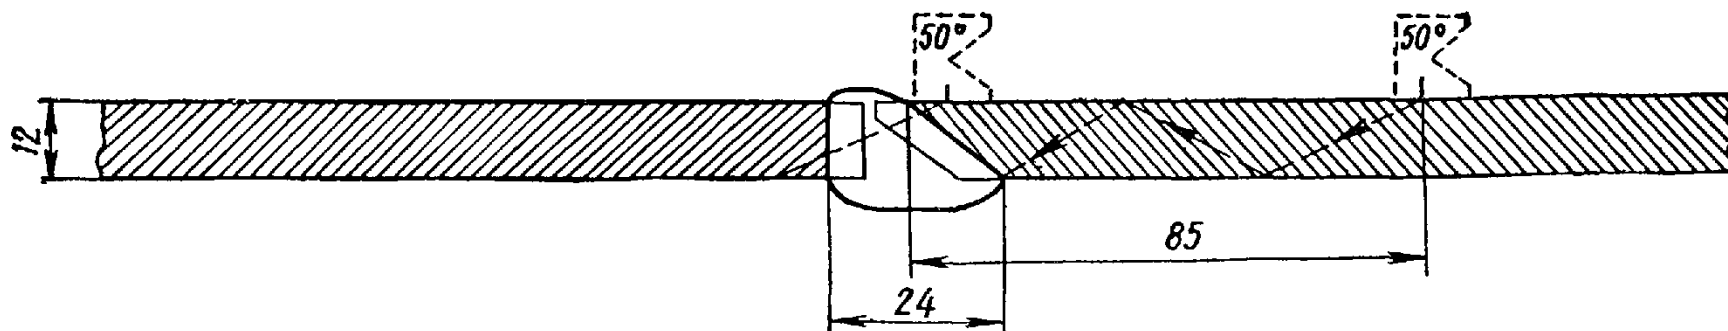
Схема контроля стыкового сварного шва в стали толщиной 12 мм
